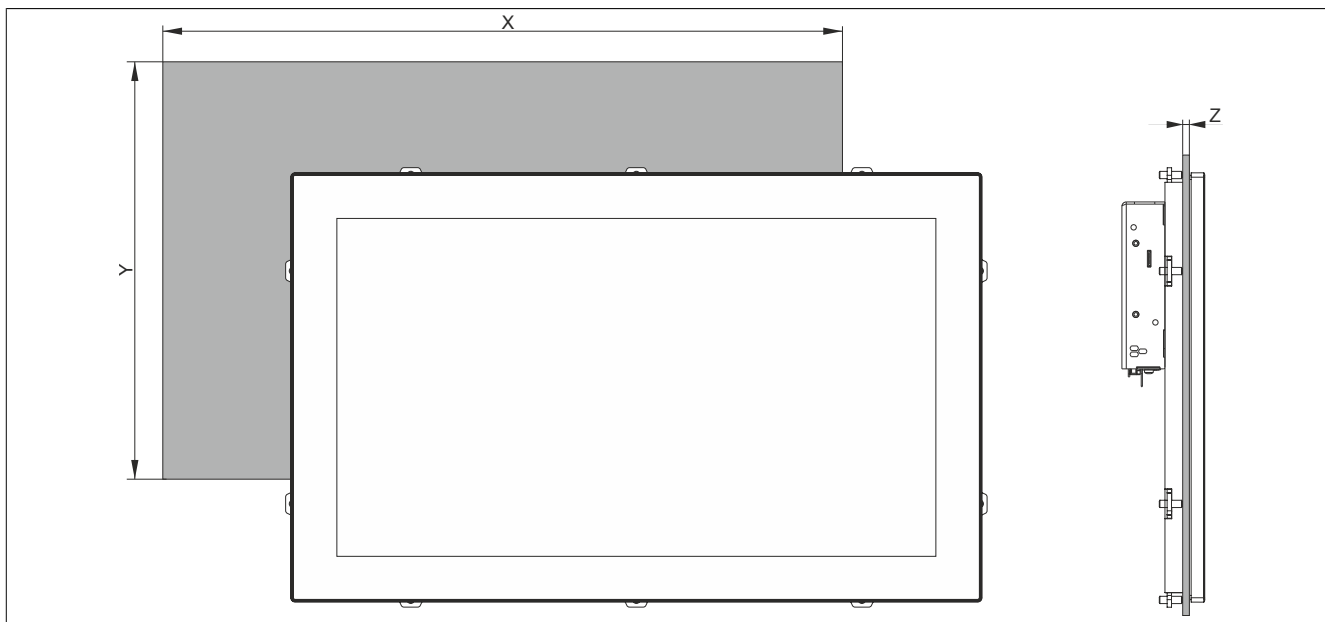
Устройство Panel PC 2200 на базе панелей AP9x3 — монтажный чертеж
